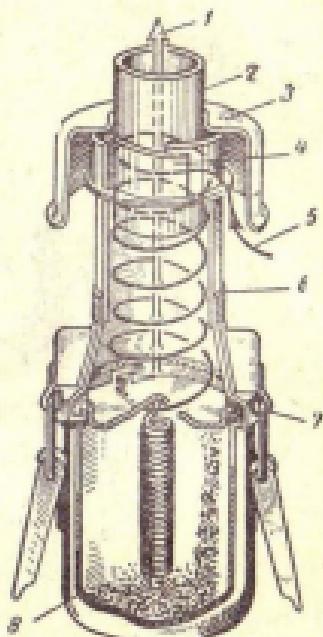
Воздухоочиститель: 1 — направление движения очищенного воздуха; 2 — патрубок; 3 — отражатель; 4 — спиральные лопатки; 5 — струя атмосферного воздуха; 6 — воронка; 7 — крышка; 8 — пылеуборщик.
